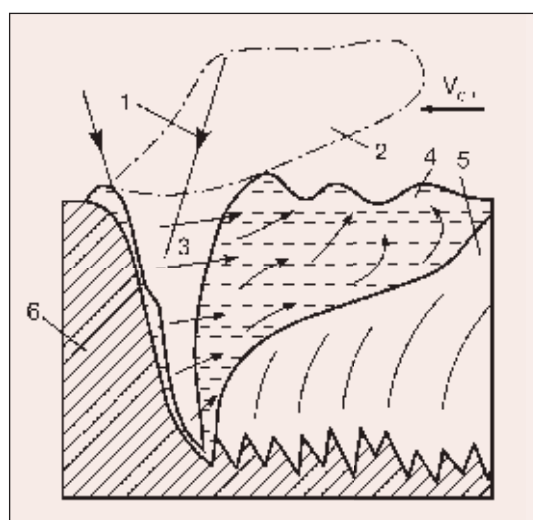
Схема продольного сечения сварочной ванны: 1 — лазерное излучение; 2 — плазменный факел; 3 — парогазовый канал; 4 — хвостовая часть сварочной ванны; 5 — закристаллизовавшийся металл; 6 — свариваемый материал
